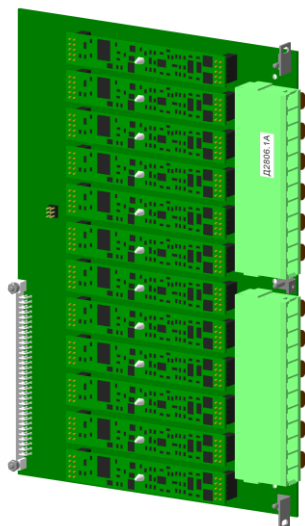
Внешний вид блока типа Д280Х(А)
